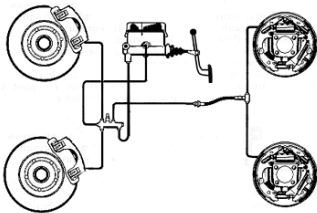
Systèmes de freinage à double circuit avant/arrière
